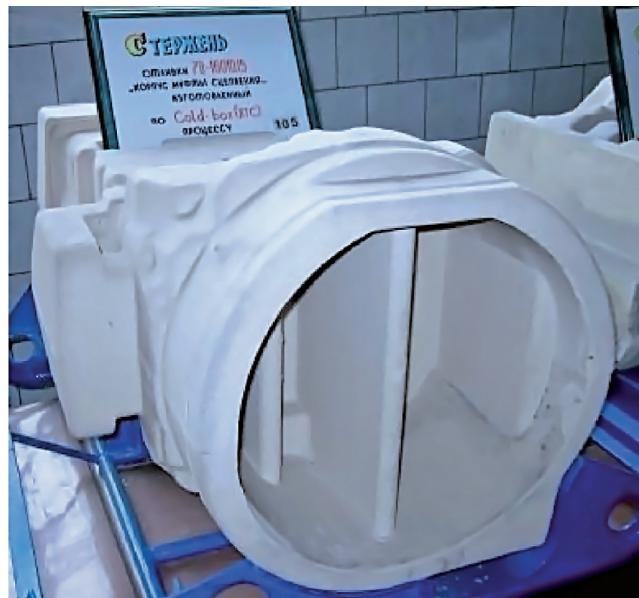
Целиковый стержень отливки «корпус муфты сцепления 70-1601015», изготовленный по Амин-процессу
